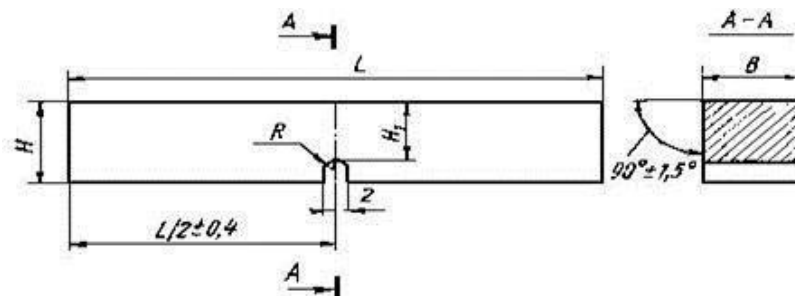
Образец с U-образным надрезом для испытаний на ударный изгиб
